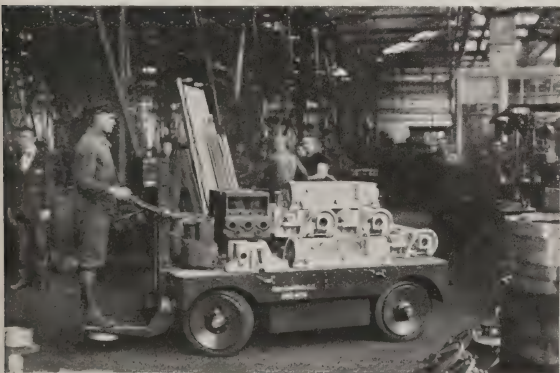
Der Elektrokarren in einer Maschinenfabrik
